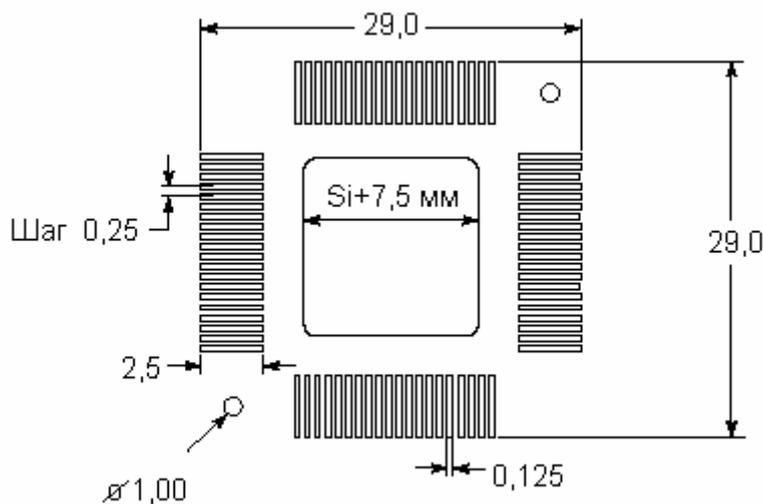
Габаритные размеры посадочного места на ПП для установки корпуса TAB на 80 выводов. Размеры в мм.
